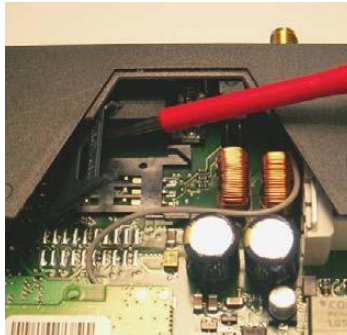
Levantar la pieza superior del SINAUT MD720-3.
